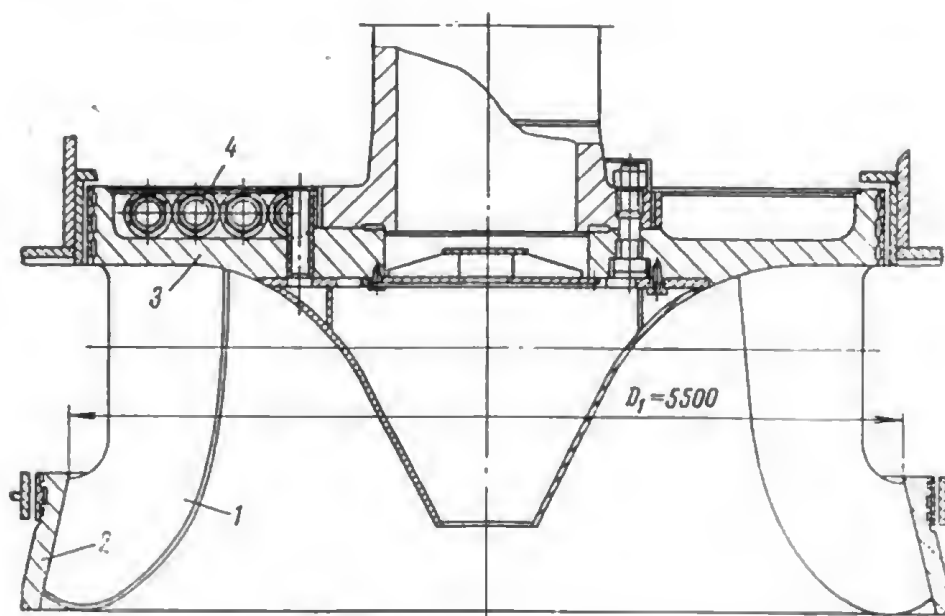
Сварно-литое рабочее колесо радиально-осевой турбины.
